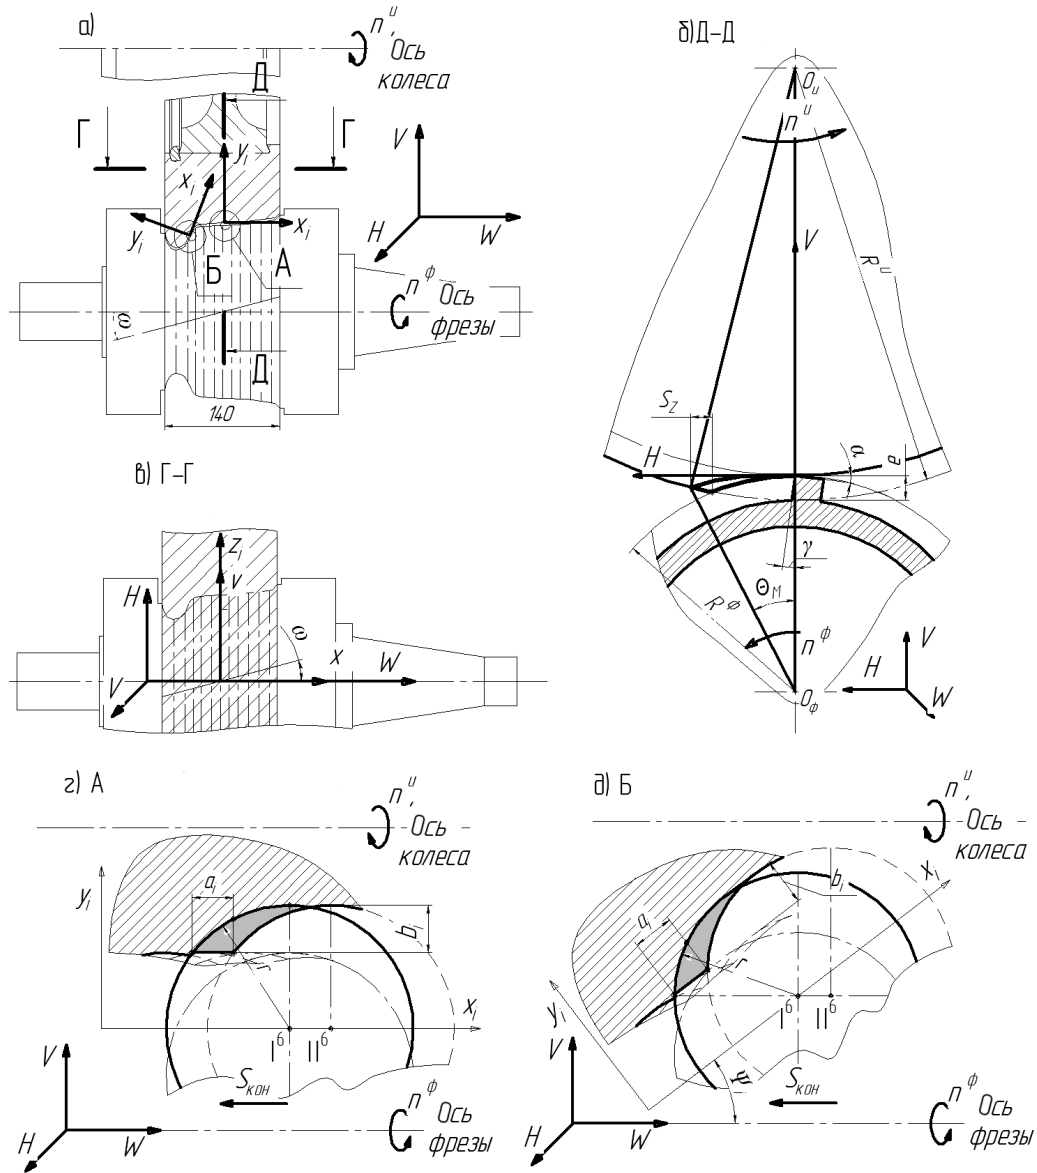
Обработка колесной пары на фрезерном станке: а, з, д – вид в основной плоскости; б – вид в рабочей плоскости; в – вид в плоскости резания; x_i, y_i, z_i – подвижная система координат, связанная с режущим зубом; n^u – частота вращения колеса, об/мин; n^ϕ – частота вращения фрезы, об/мин; R^u – внешний радиус обрабатываемого изделия, мм; R^ϕ – внешний радиус фрезы, мм; e – глубина врезания, мм; γ – главный передний угол, град.; α – главный задний угол, град.; S_z – подача на зуб фрезы, мм/зуб; Θ^M – максимальный угол контакта фрезы с обрабатываемым колесом, град.; b – ширина срезаемой стружки, мм; a – толщина срезаемой стружки, мм; Ψ_i – угол наклона образующей поверхности
